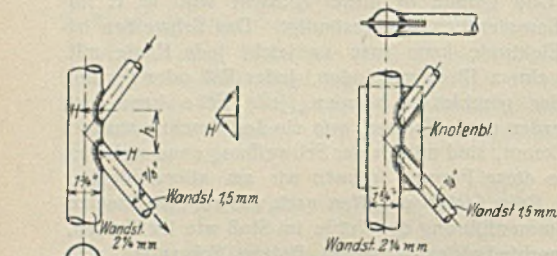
a u. b. Verbesserungsvorschlag einer geschweißten Knotenpunktausbildung.
